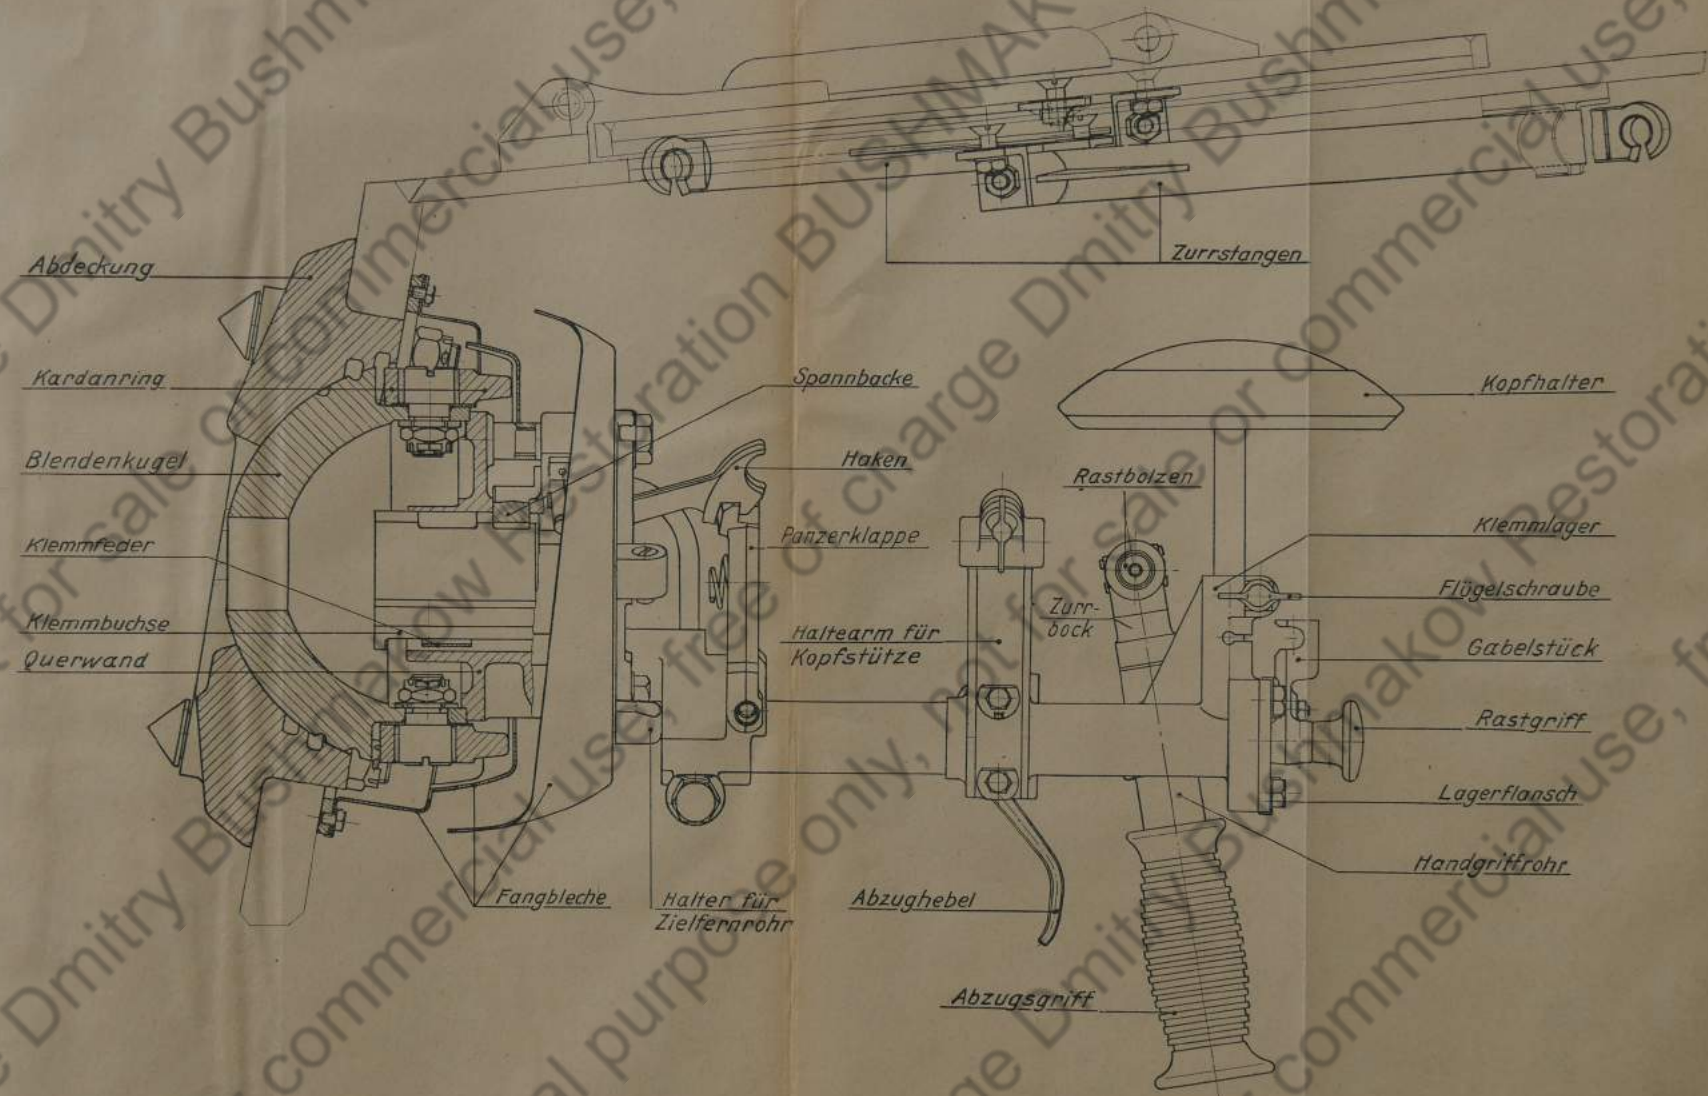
Kugelblende 30 für MG 34 mit Curtzführung, Schnitt- und Seitenansicht, Ausf. E
